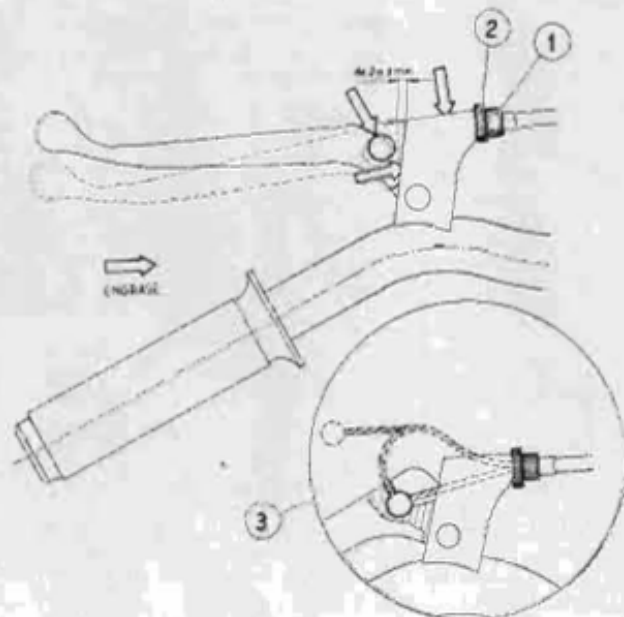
Mando embrague: Reglaje, engrase y cambio del cable.
